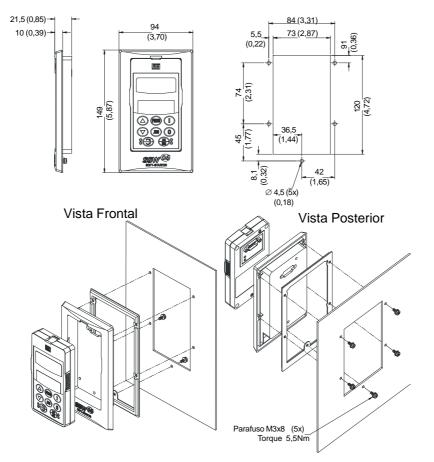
Dimensões da HMI em mm (in) e como instalar no painel com moldura
